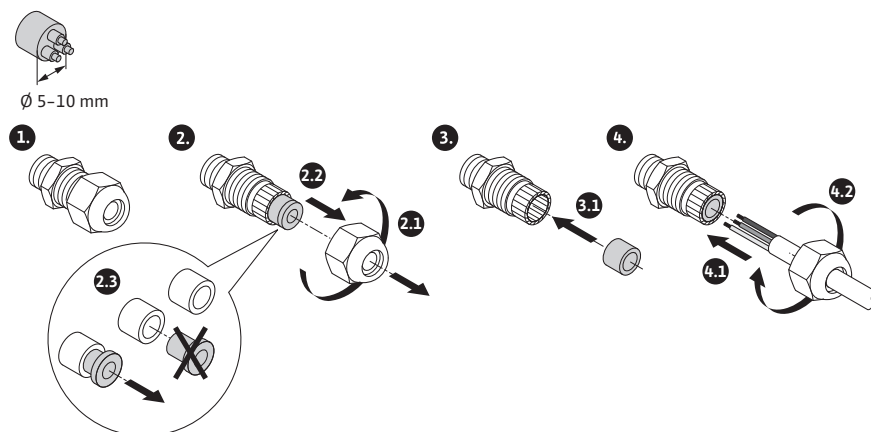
Passe-câbles à vis \varnothing 5-10 mm
